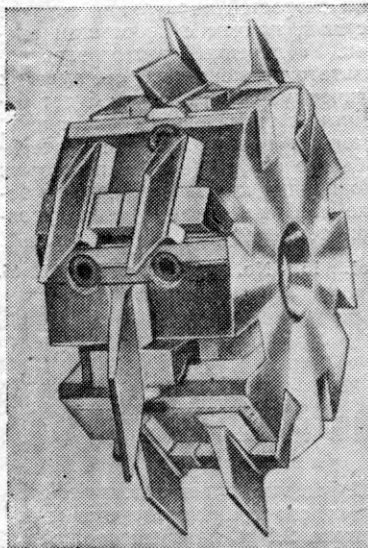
Ножевая головка для нарезки зубчатых шипов
